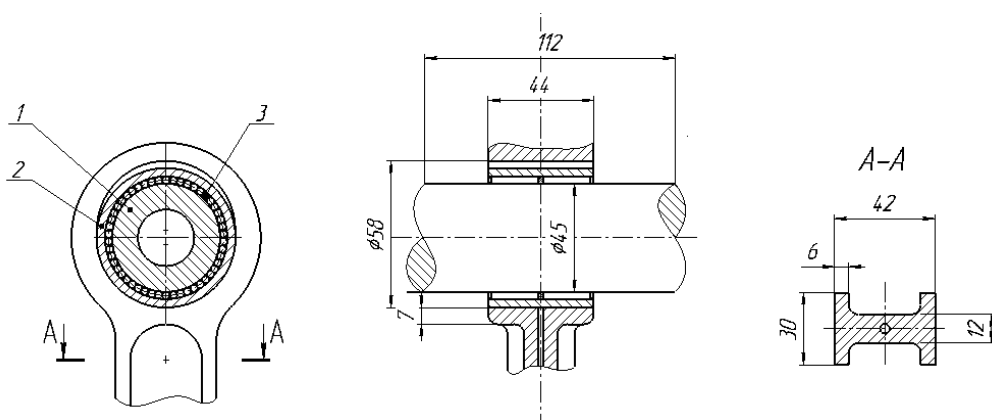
Конструкція вузла ПГШ з голчастим підшипником:
